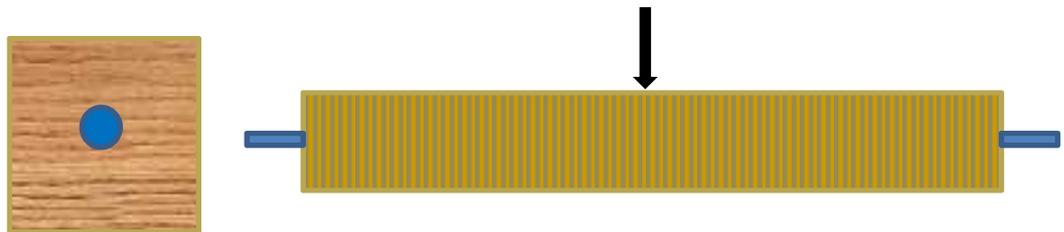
Pieza obtenida mediante LOM con una varilla metálica de refuerzo
